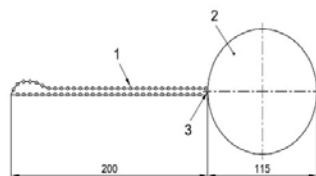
Cadena de ensayo con lazo (dimensiones en mm)
